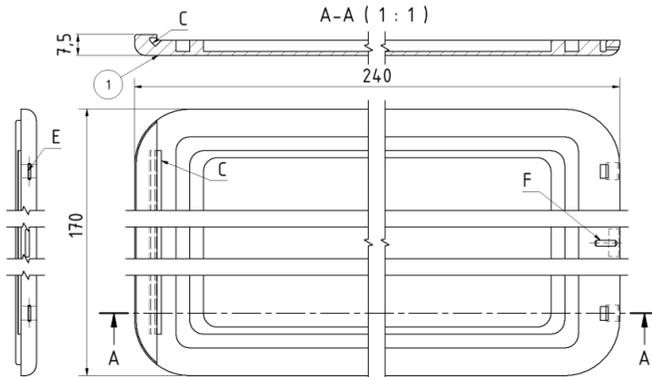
Gehäuse eines recyclinggerechten Tablet-PCs
